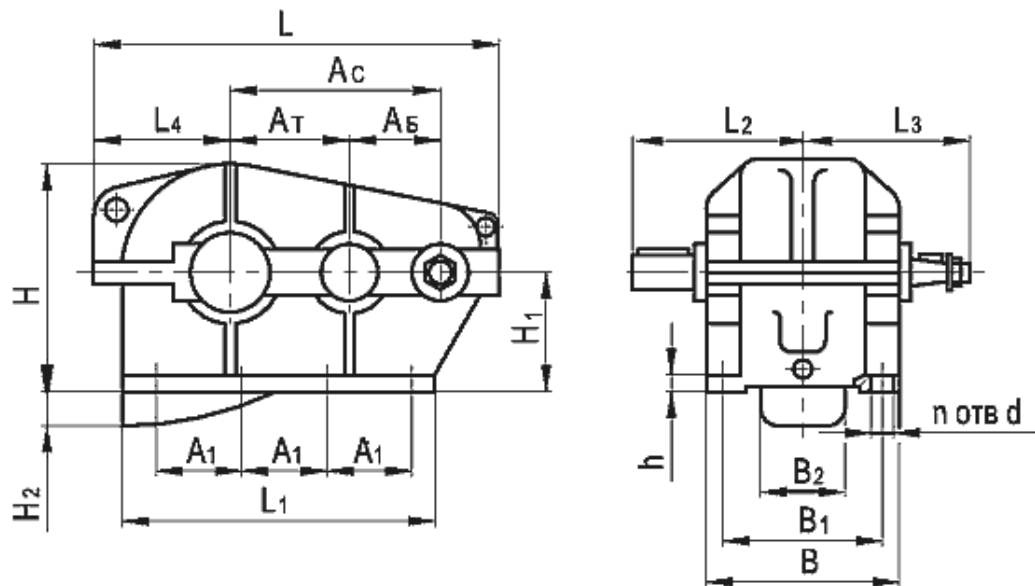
Редуктор циліндричний горизонтальний двоступінчастий крановий [6]
